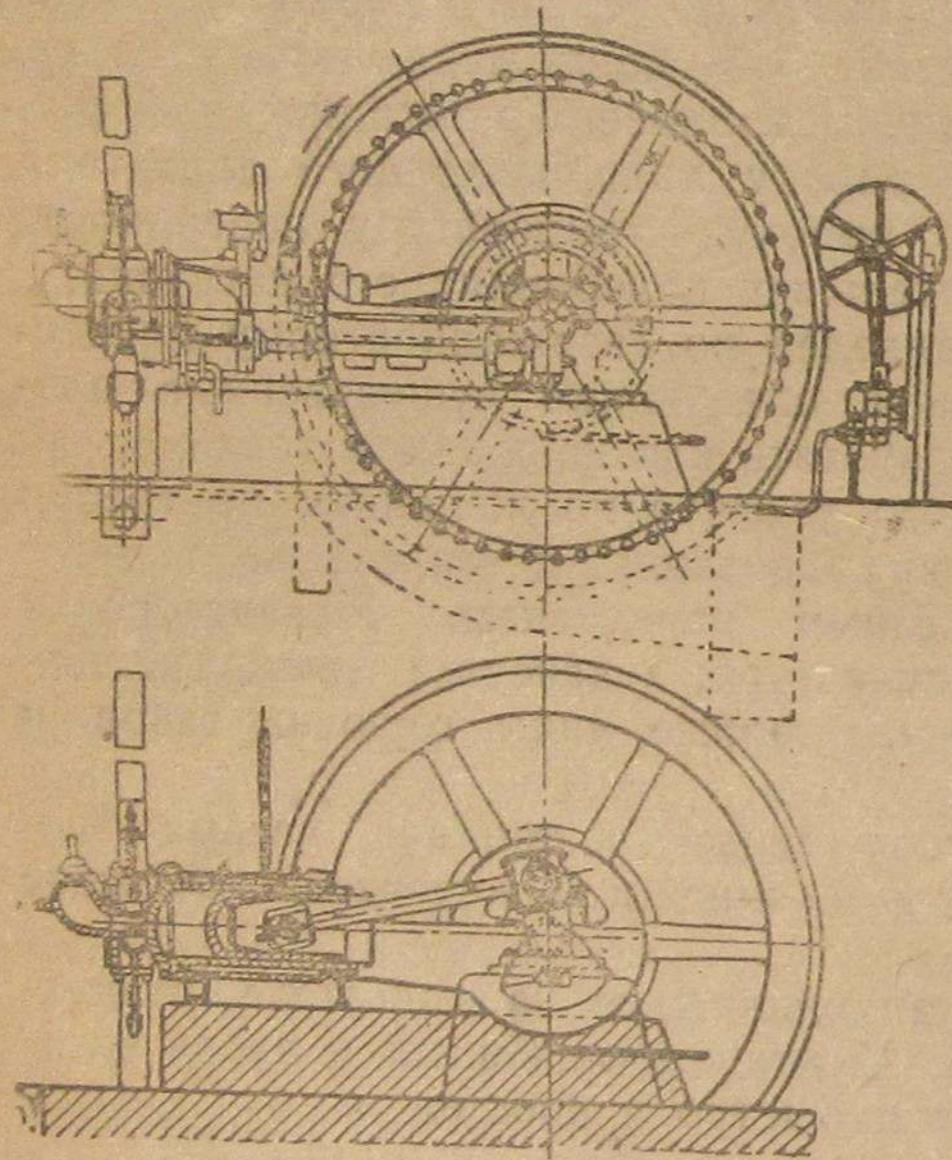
Схема газогенераторной установки для двигателя РП-40
